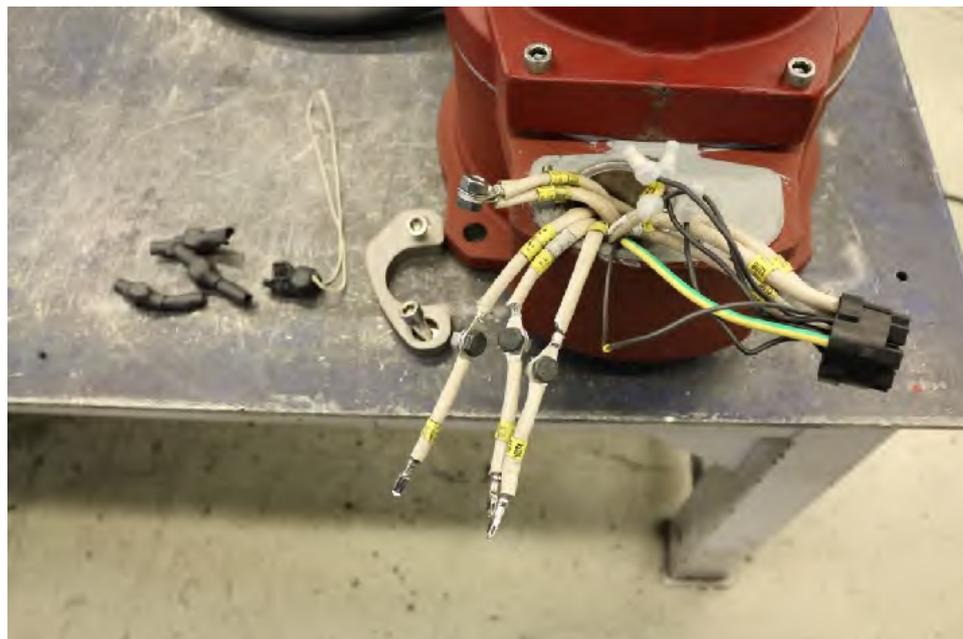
Adapterstücke und Sternpunktschaltung demontieren
